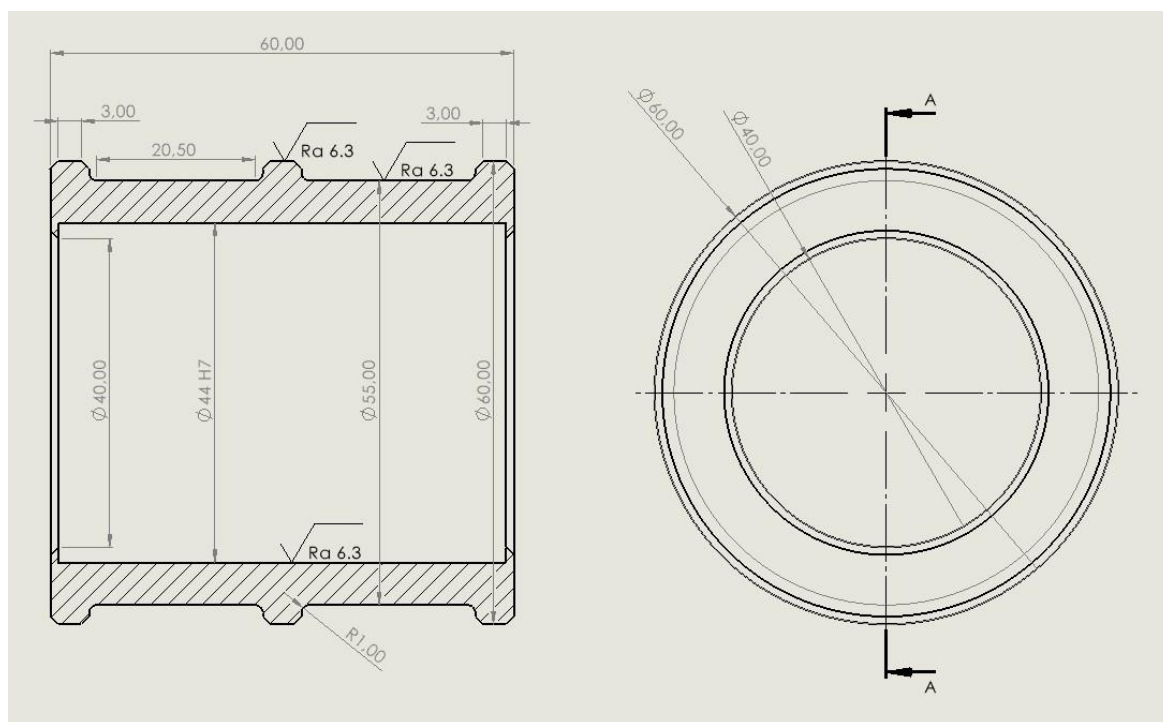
Ескіз деталі «Втулка Рухомого Механізму»
